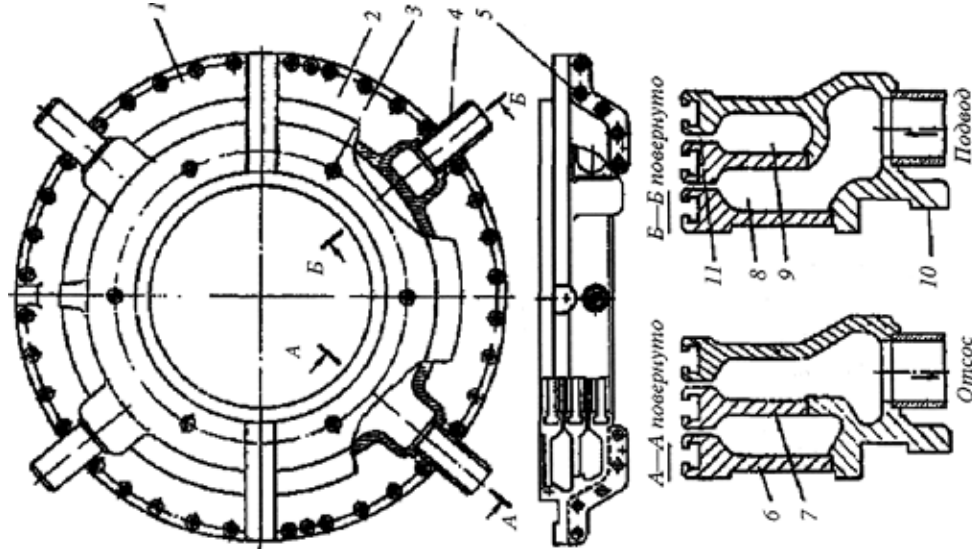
Сварно-литой корпус концевого уплотнения турбины К-500-240 ХТЗ: 1, 2 – верхняя и нижняя части корпуса; 3 – стержень-стяжка; 4 – труба; 5 – болт; 6, 7 – профильные кольца; 8 – камера подвода уплотняющего пара; 9 – камера отсоса паровоздушной смеси; 10 – присоединительный плоский фланец; 11 – кольцевая щель
